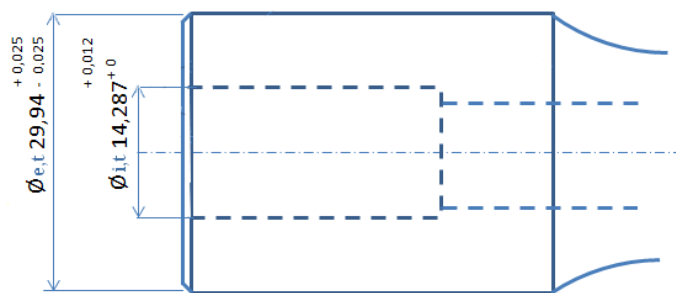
Géométrie et dimensions des têtes d'éprouvette
